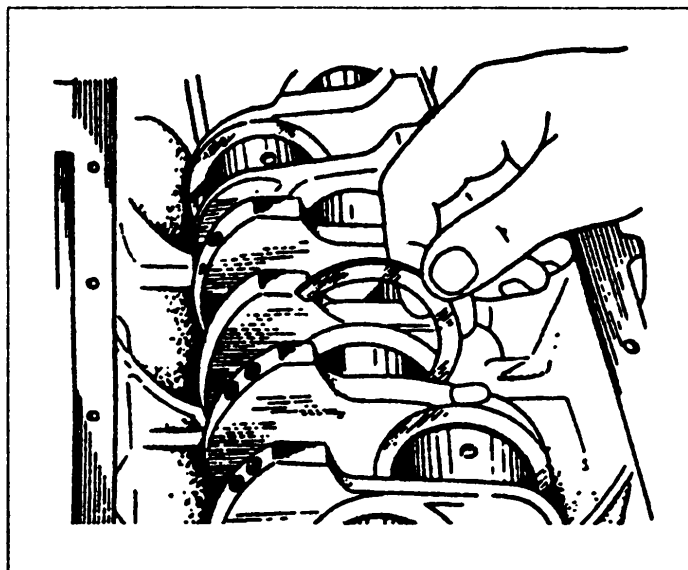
Установка упорных полуколец коленчатого вала в гнезда среднего коренного подшипника
